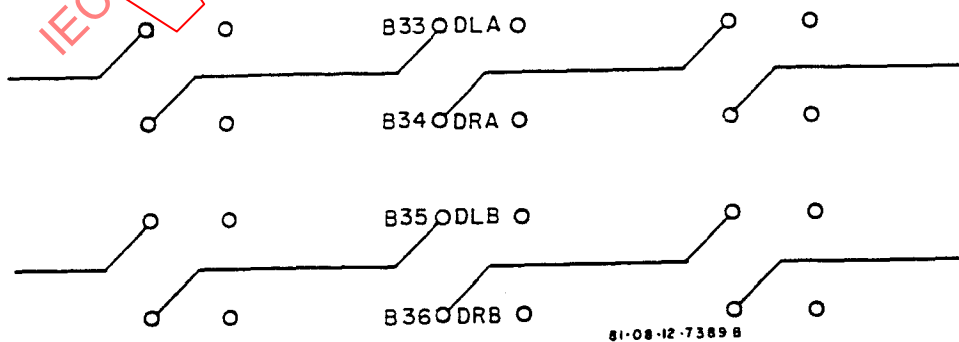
Câblage de la guirlande du fond de panier. (vu du devant du châssis)
